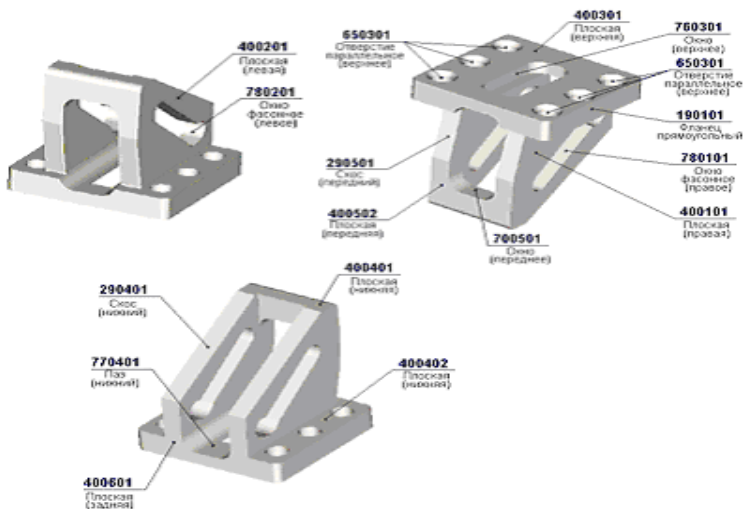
Кодирование поверхностей корпусной детали «Кронштейн»
